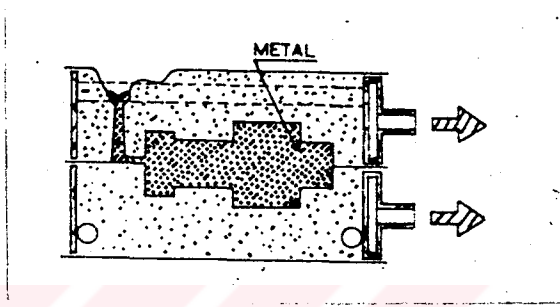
Kalıplama kutusunada vakum uygulanması ve sert kum kalıp elde edilmesi /2/.
